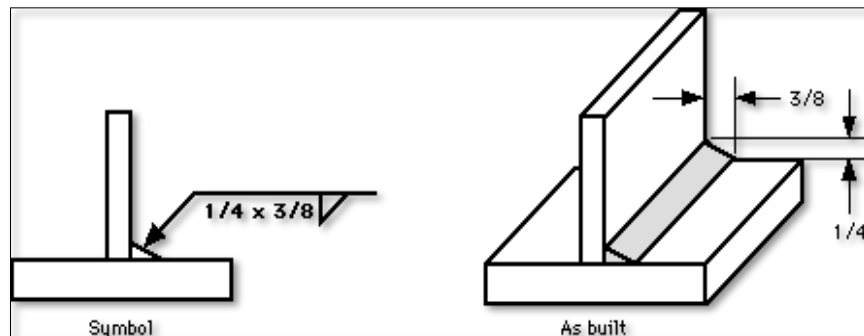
Soldadura de filete de dos caras desiguales.
